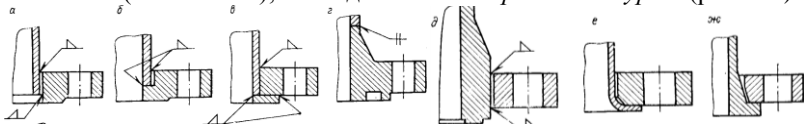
Основные виды фланцев: а÷в – плоские приварные; г – типа "шип-паз"; д – с "шейкой"; е – с отбортовкой; ж – с буртом
